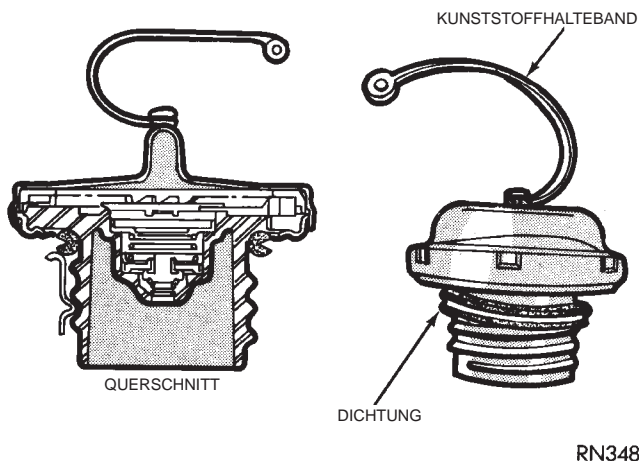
Tankdeckel mit Über- und Unterdruckausgleich
